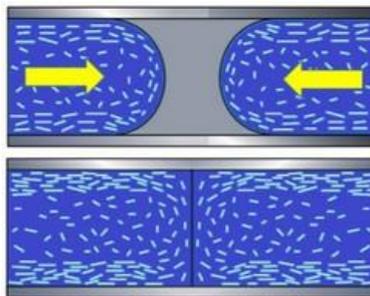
Línea de soldadura. (Fuente:[12])
